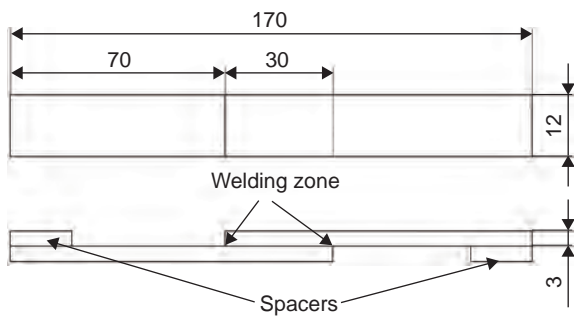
7075/6061 铝合金焊接试件尺寸
